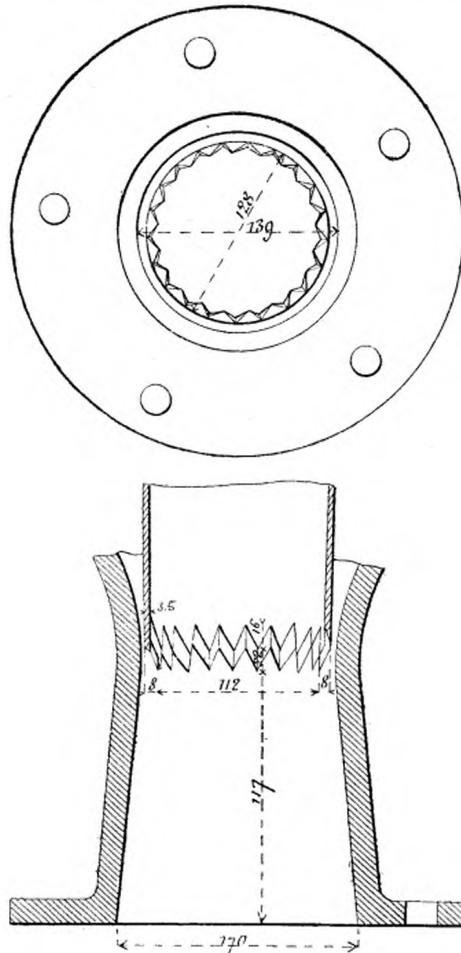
Coupe et plan par-dessous de l'extrémité d'une tuyère
